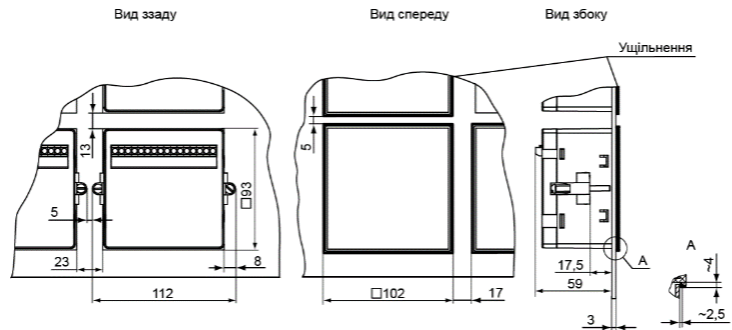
Пристрій у корпусі Щ1, встановлений у щит завтовшки 3 мм
